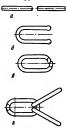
Эскивы переходов при ковке цепи; а — рубка заготовки; б — гибка заготовки и высадка концов; е — расплющивание и гибка концов; е — кузшечивя сварка.
